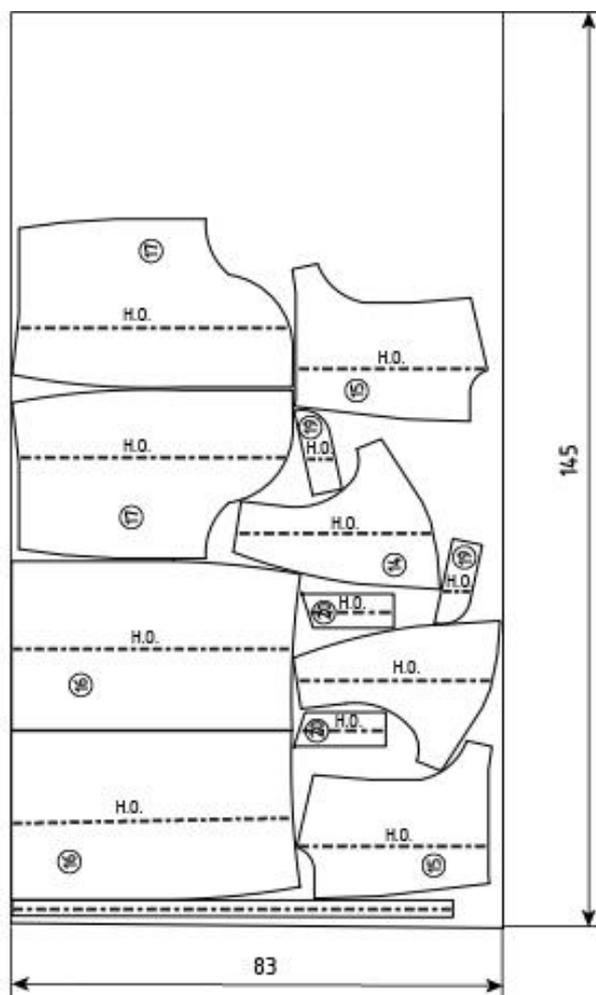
Схема раскладки лекал на подкладочной ткани
